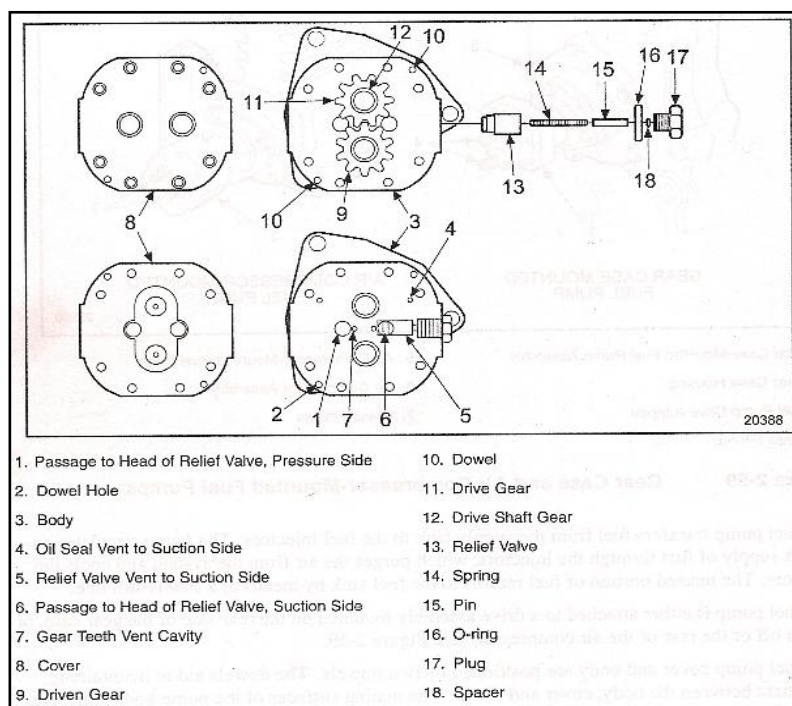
Partes de la Bomba de Combustible, Vista Frontal.⁷
